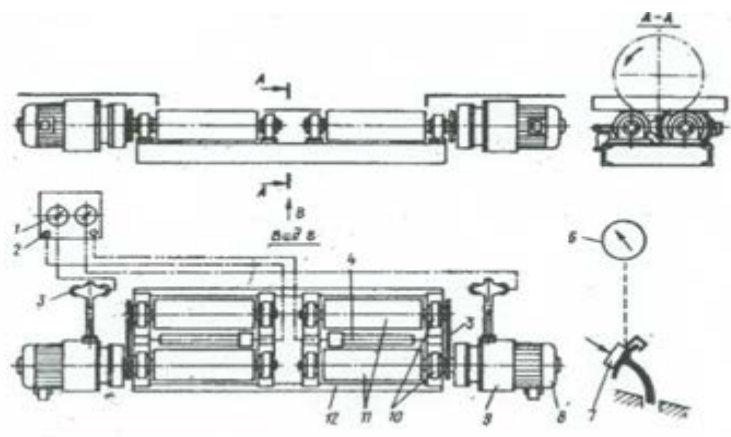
Типовая схема силового тормозного стенда: 1-измерители тормозных сил; 2-световые индикаторы блокировки колес; 3-датчик тормозной силы; 4-вспомогательный антиблокировочный ролик; 5-цепная передача; 6-измеритель давления на педаль; 7-датчик давления на педаль автомобиля; 8-электродвигатель; 9-редуктор; 10-подшипник; 11-ролик; 12-рама
